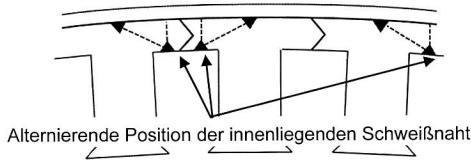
Variante 4 mit alternierender innenliegender Schweißnahtposition im Zusammenbau
